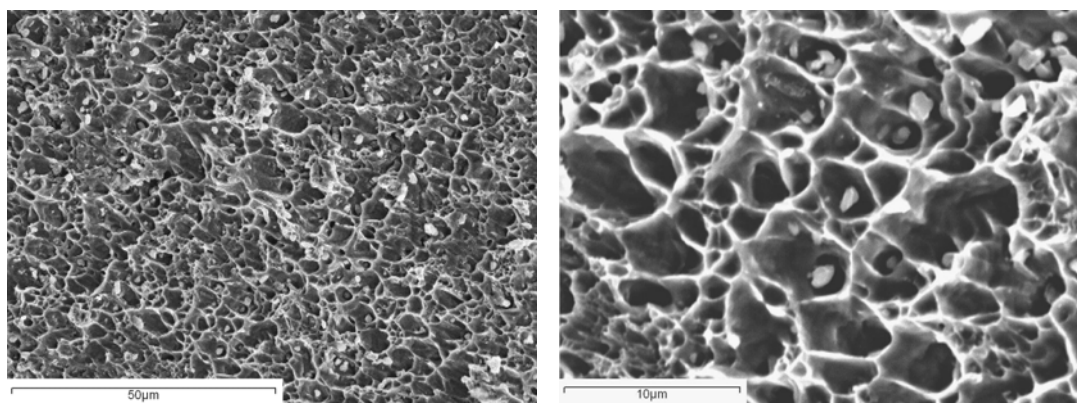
Superficie de fractura de la unión realizada a 825° C durante 30 minutos.
